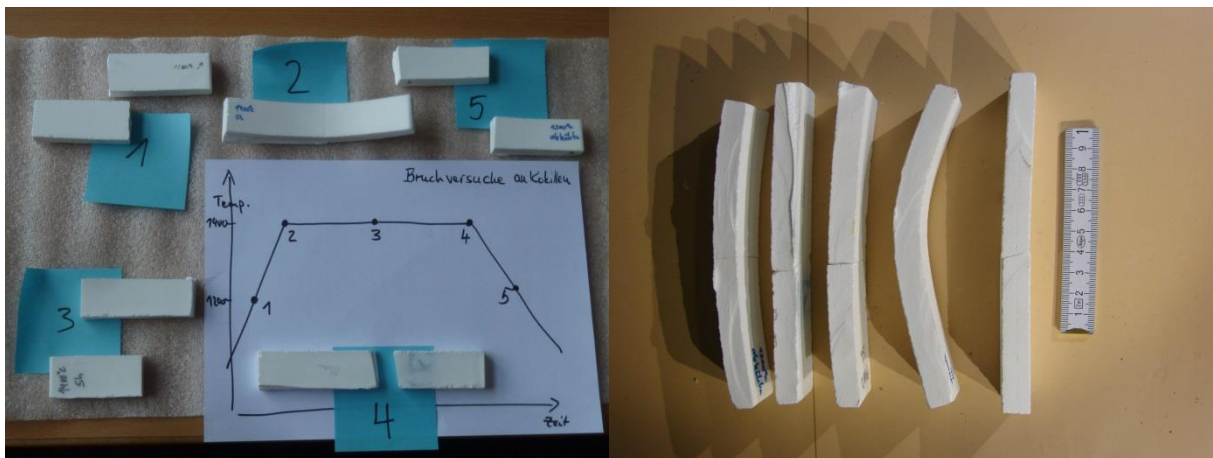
Kokillenstücke nach Durchführung der Bruchversuche
